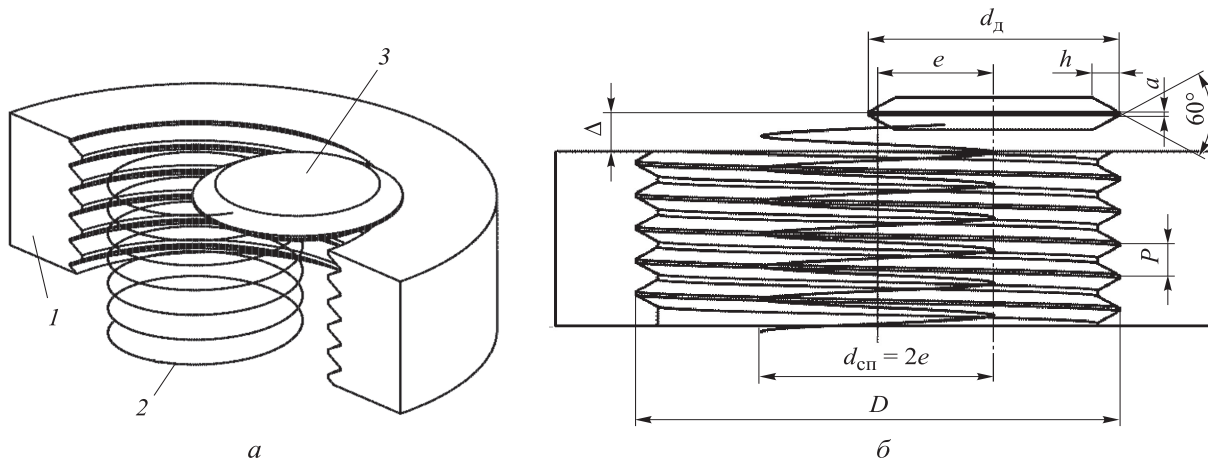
Геометрическая модель кинематической схемы формообразования внутренней резьбы: а — фрезерование внутренней резьбы (1 — заготовка с резьбой; 2 — траектория движения инструмента; 3 — модель дисковой резьбовой фрезы); б — параметры модели
